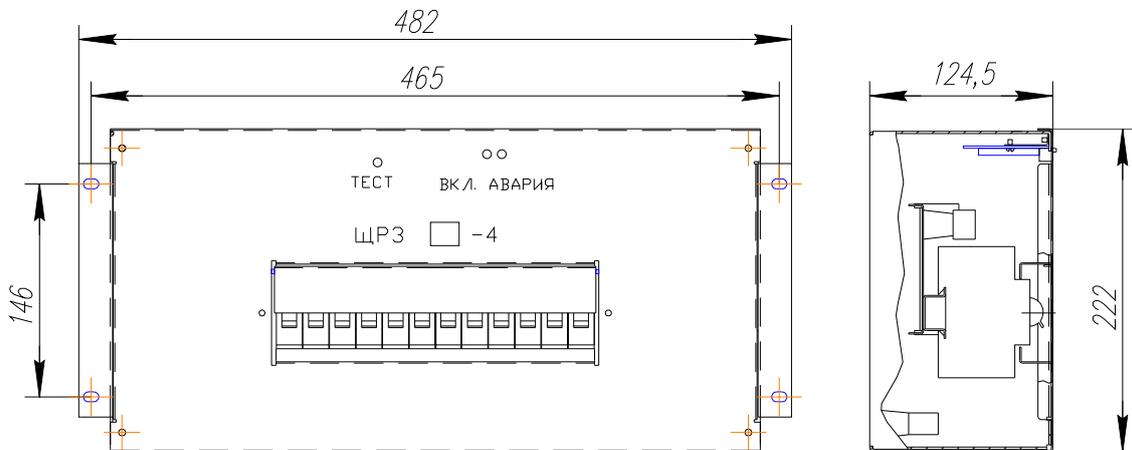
Габаритный чертеж щитов ЩРЗ 24-4(С), ЩРЗ 48-4(С), ЩРЗ 60-4(С)
